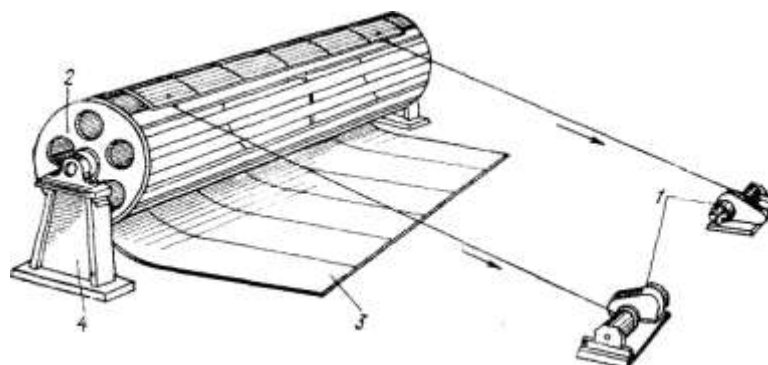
Поворотное приспособление для кантовки полотнищ на 180°
